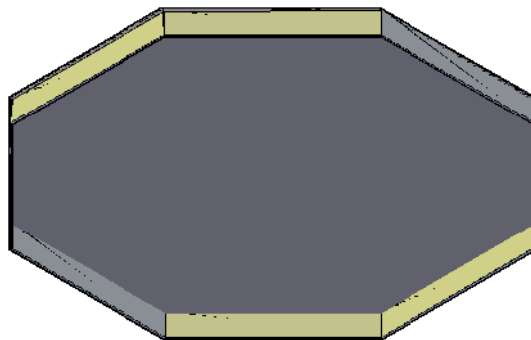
Diseño 3D de las tapas para el sellado hermético.
